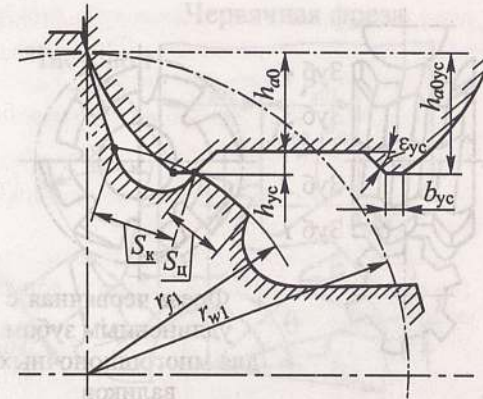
Размеры зубьев червячной фрезы с «усиками»
